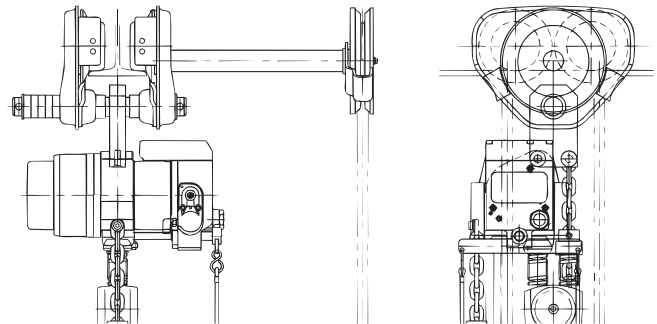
Montaje con lengüeta en el TS2 con engranaje y rueda manual extendida
